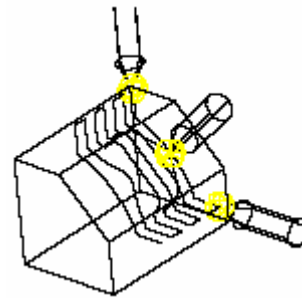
Trajectoire en zigzag iso-paramétrique, machine outil CNC à 5 axes. [BEN 02].
